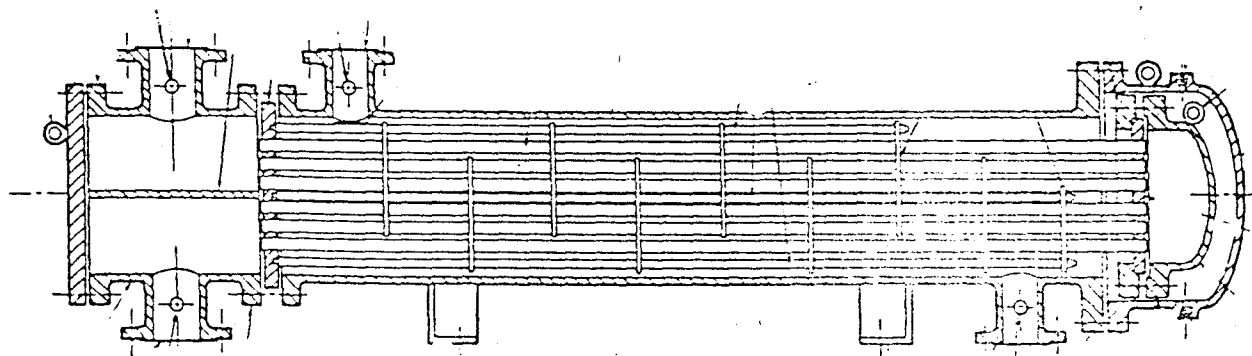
Fixed-tubesheet exchanger with integral channel
